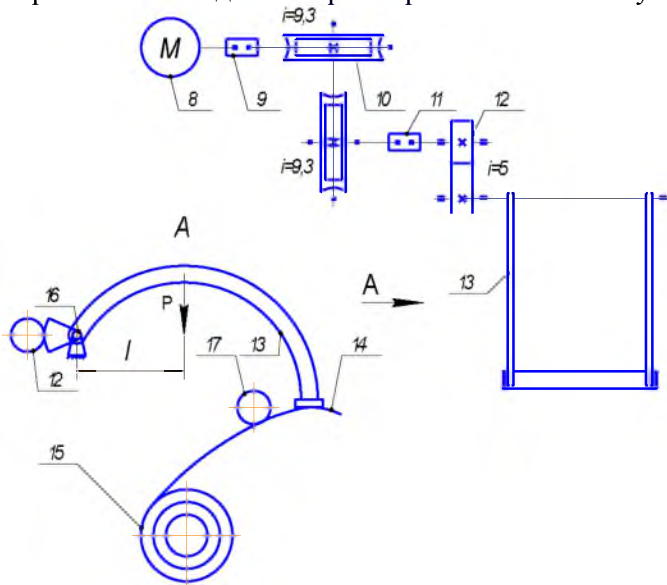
Кинематическая схема привода отгибателя конца полосы
